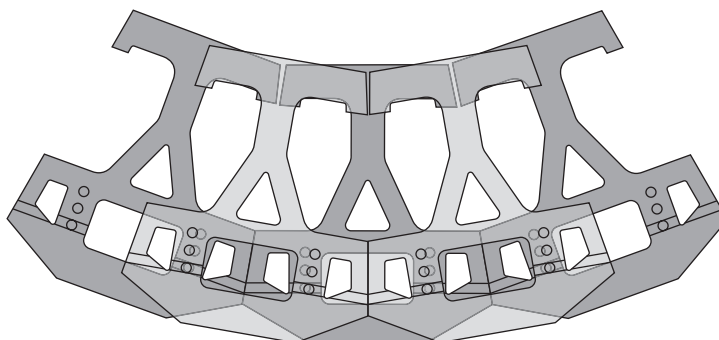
Skladba svislého oblouku s minimálním poloměrem
